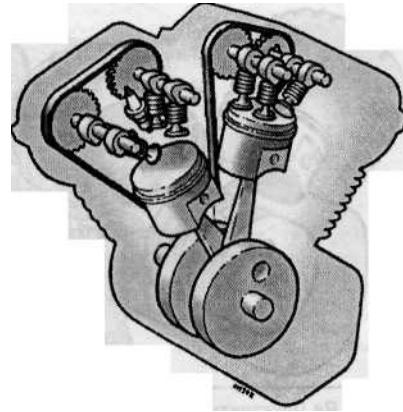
Вb Четырехтактный V-образный двухцилиндровый двигатель
